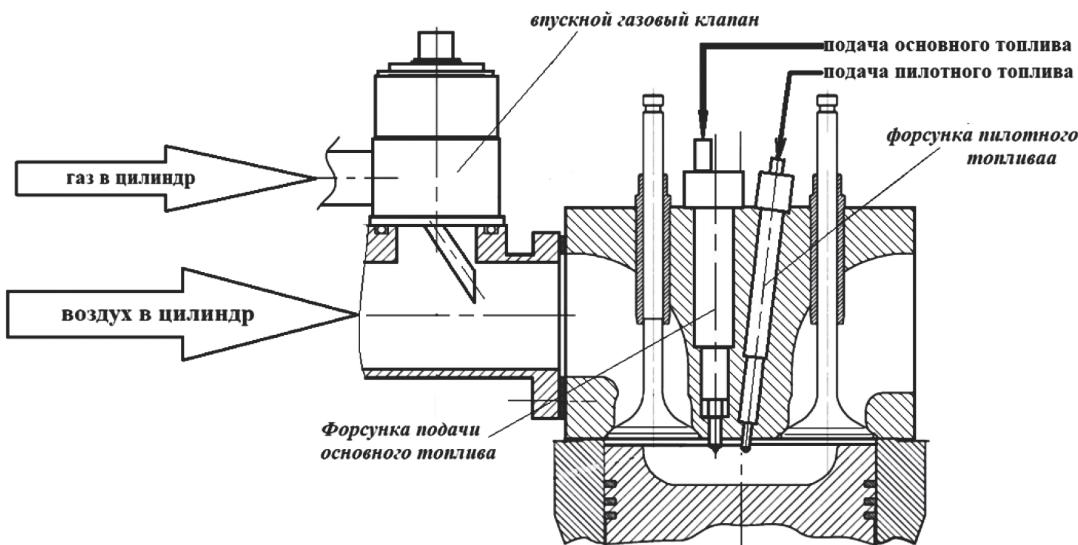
Схема двухтопливного двигателя с газом низкого давления
